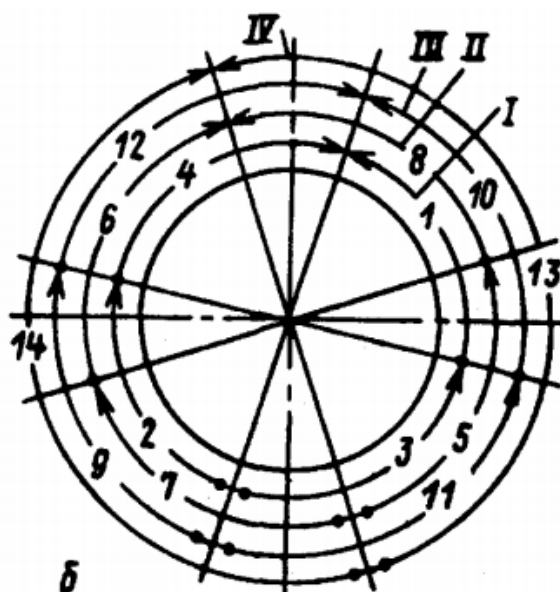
Порядок наложения слоев при сварке двумя сварщиками вертикальных неповоротных стыков труб: 1—14 – последовательность наложения участков (слоев); I—IV – слои шва
